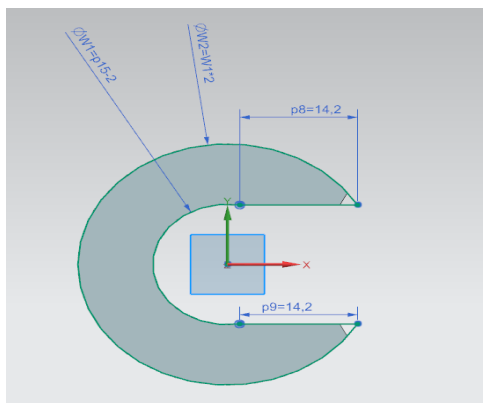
Замена размеров формулами для детали «ШАИВА»
